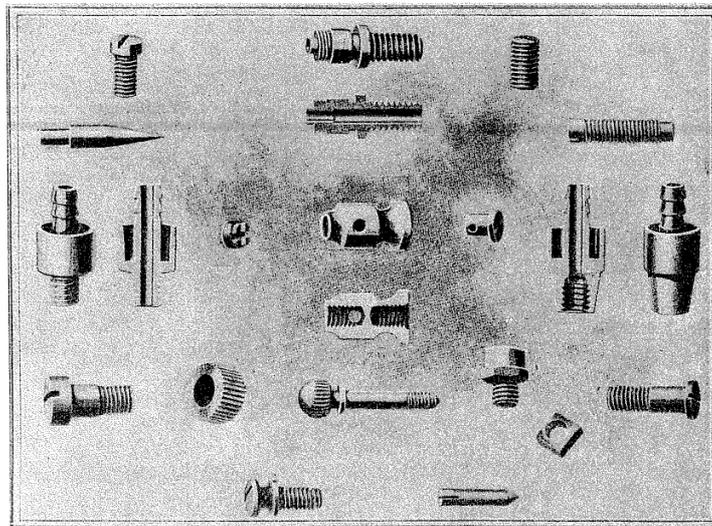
Pièces exécutés sur la machine à vis *Spencer*.
